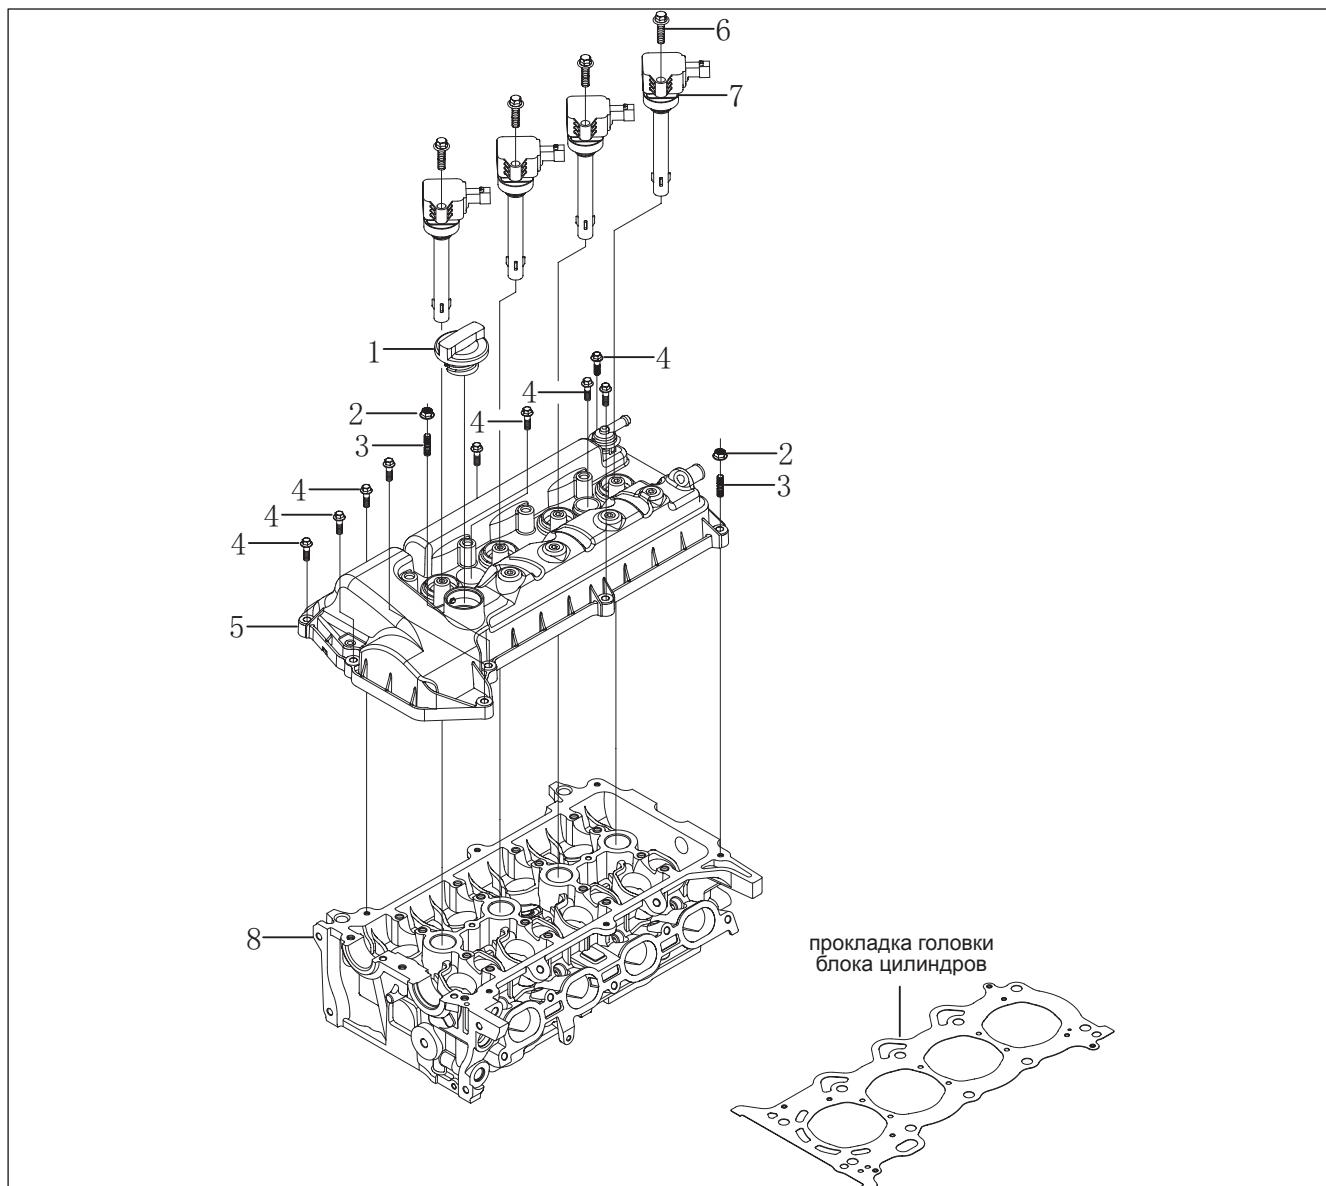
Схема расположения компонентов крышки головки блока цилиндров
